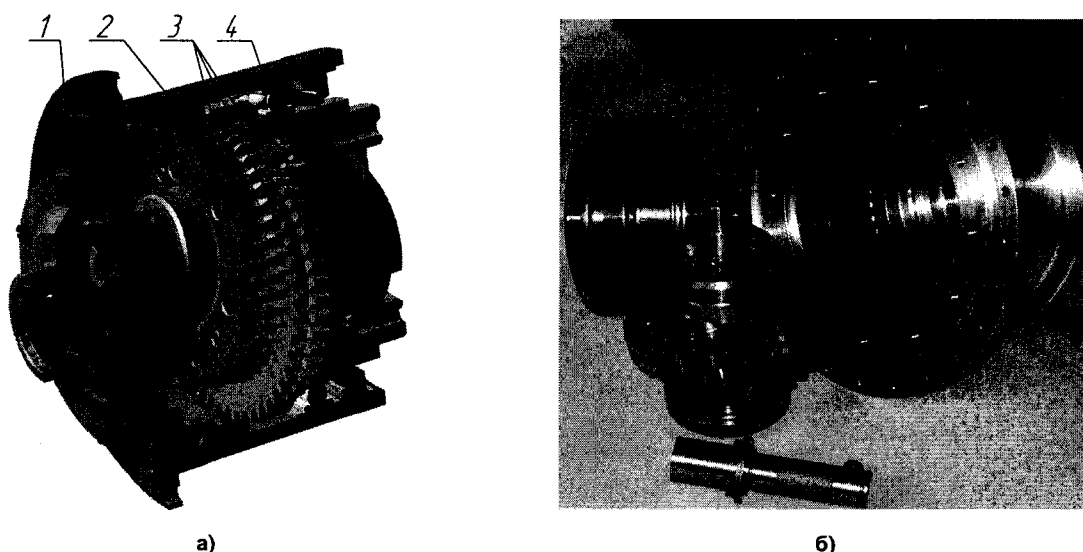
Планетарный редуктор с внутренними цилиндро-коническими зацеплениями: а – конструкция редуктора: 1 – входной вал; 2 – неподвижное эвольвентное колесо; 3 – конические шестерни; 4 – выходной вал (эвольвентное колесо); б – детали редуктора
